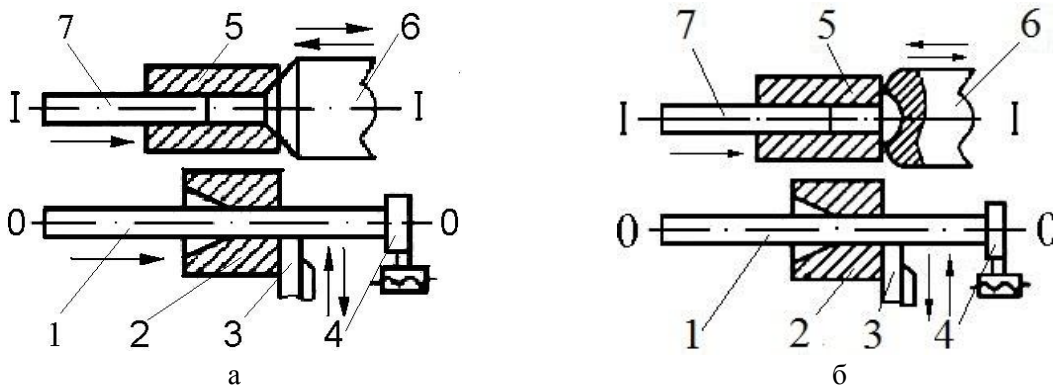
Схемы высадки заклепок: а – с потайной головкой в полость матрицы; б – с полукруглой головкой в полость пуансона: 1 – проволока; 2 – отрезная матрица; 3 – нож; 4 – упор; 5 – высадочная матрица; 6 – пуансон; 7 – выталкиватель; 0-0 – позиция отрезки; I-I – позиция высадки
